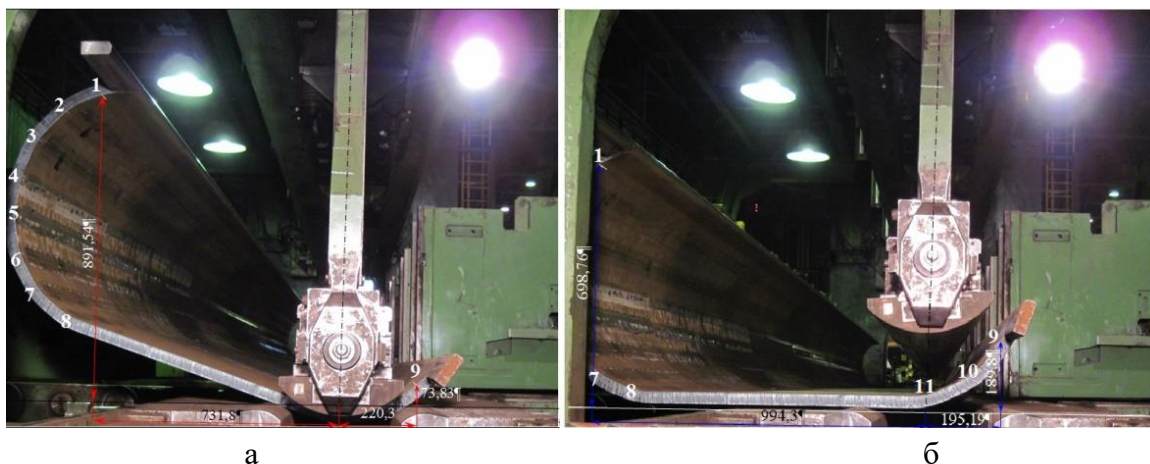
Фотокадры трубной заготовки на 11 шаге формовки
